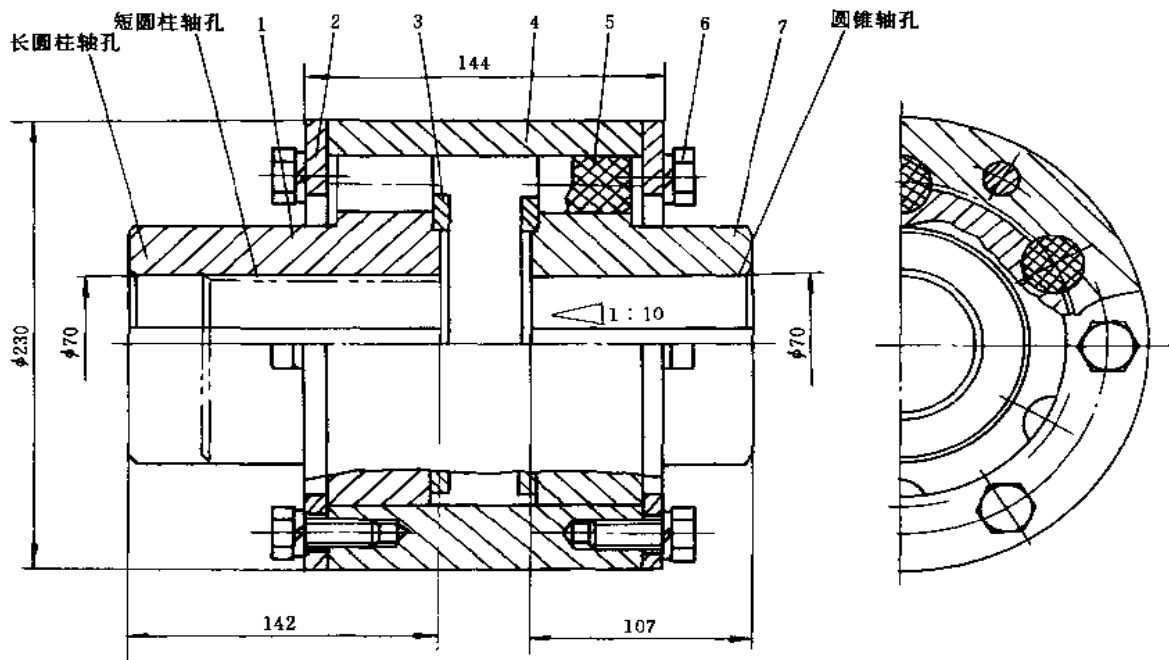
圆锥轴孔弹性柱销齿式联轴器 (ZLD 型)
